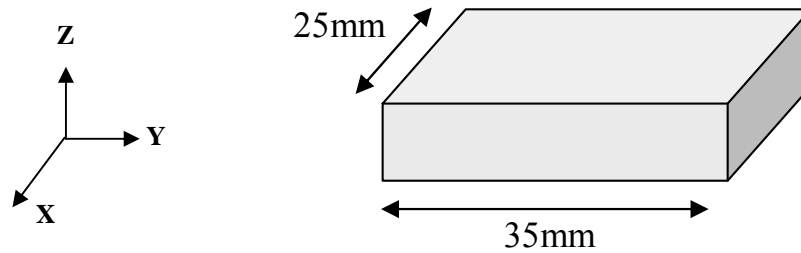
Géométrie des éprouvettes de cyclage thermique
